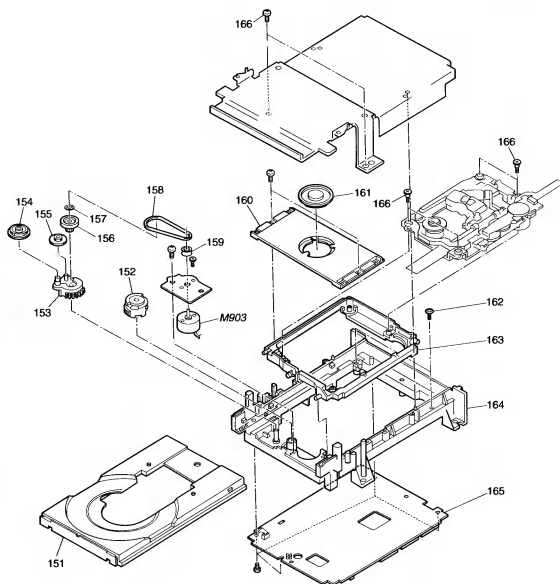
Сборочный чертеж устройства загрузки дисков моделей DVP-S715, S7700, K800D
